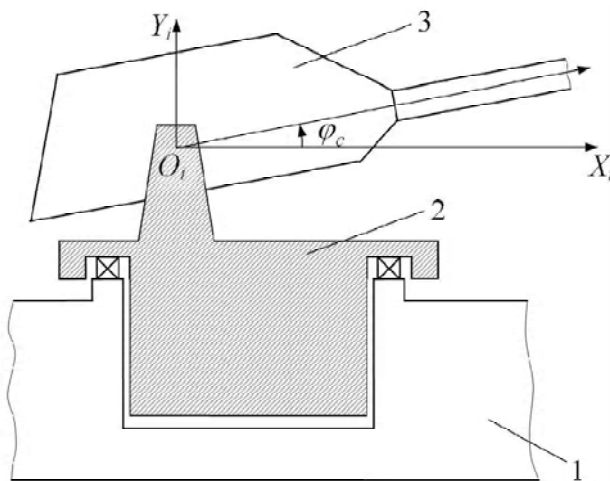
Кинематическая схема взаимного расположения модуля вооружения и башенки на корпусе БМ:
